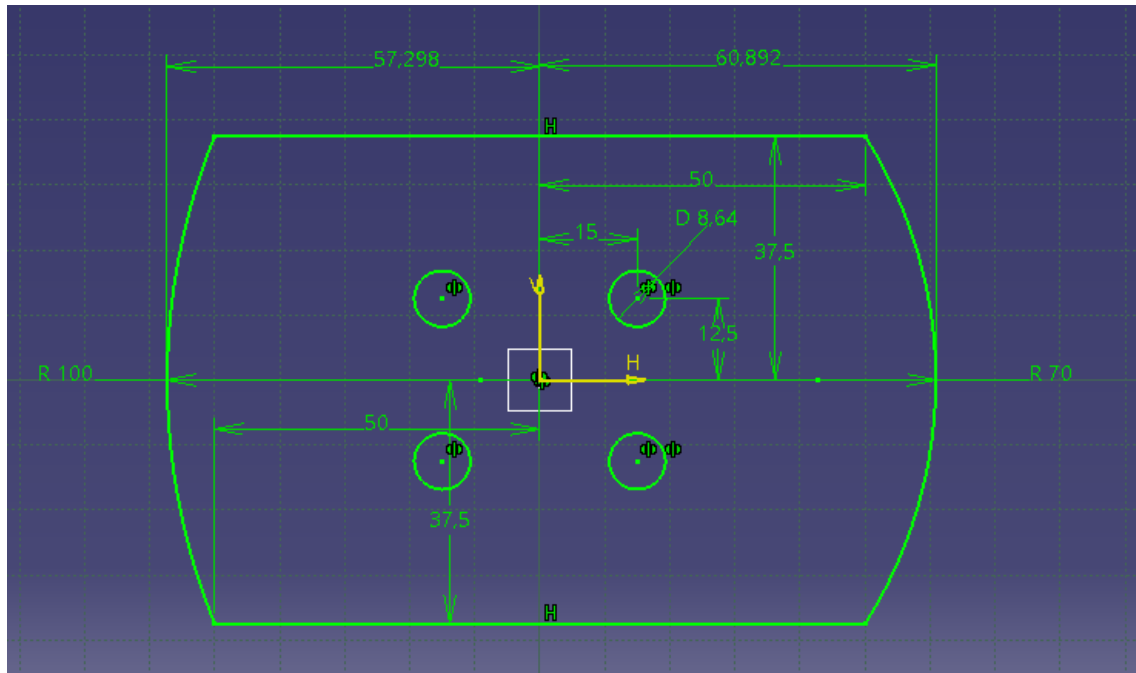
Dimensiones matriz; FUENTE: [Propia]
